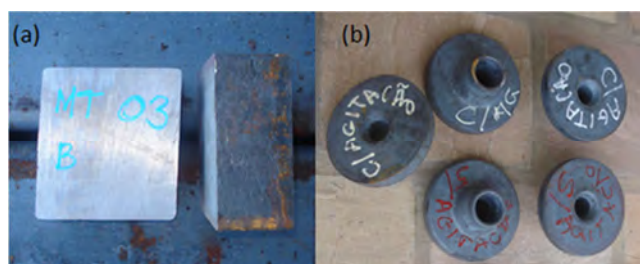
Billets de seção quadrada para o forjamento de flanges (a) e flanges forjados e rebarbados (b).
